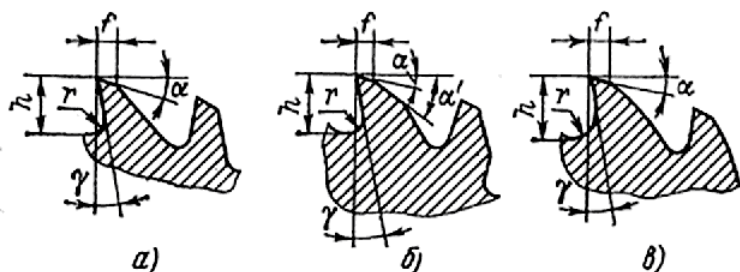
Формы спинки зуба цельных быстрорежущих фрез
